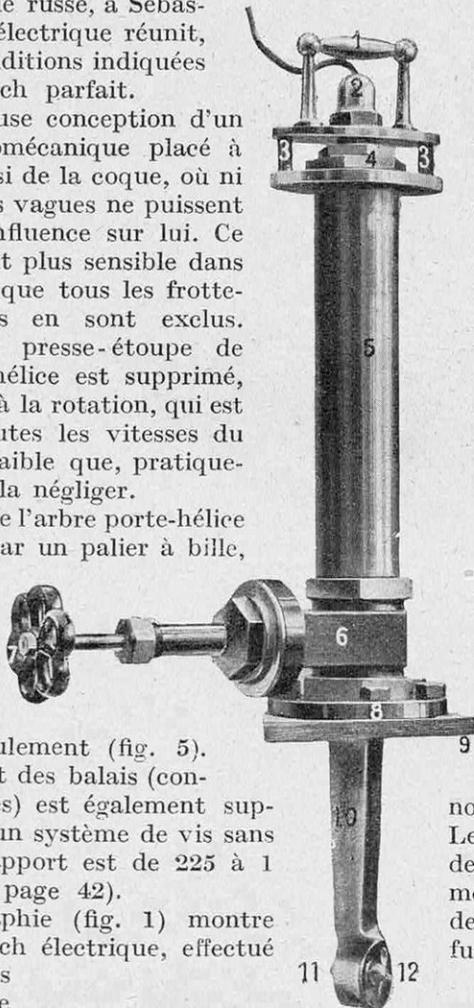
VUE D'ENSEMBLE DU LOCH ÉLECTRIQUE
